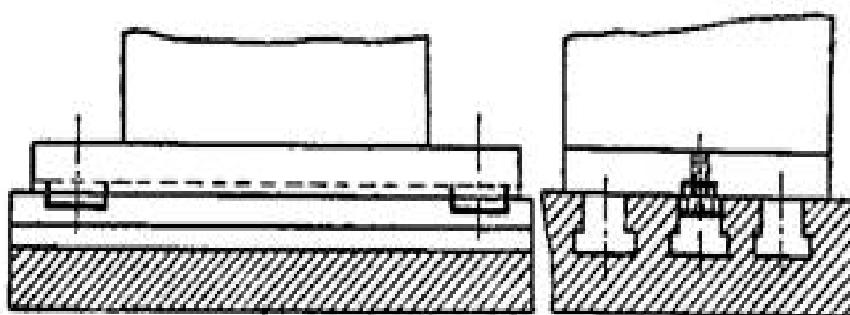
Схема ориентирования приспособления на столе станка с помощью шпонок, закрепленных на корпусе
